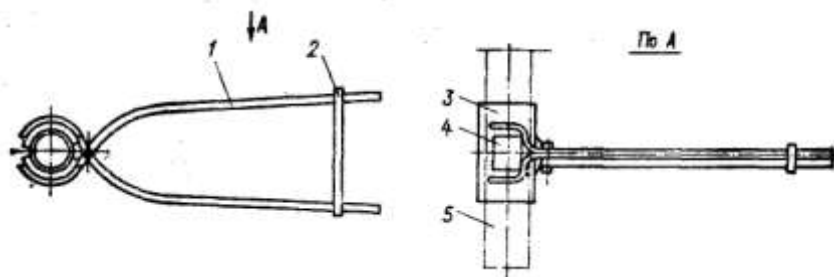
Клещи для центровки труб 1 — рукоятка; 2 — хомут стопорный; 3 — накладка; 4 — окно для прихвата; 5 —стыкуемые, трубы
